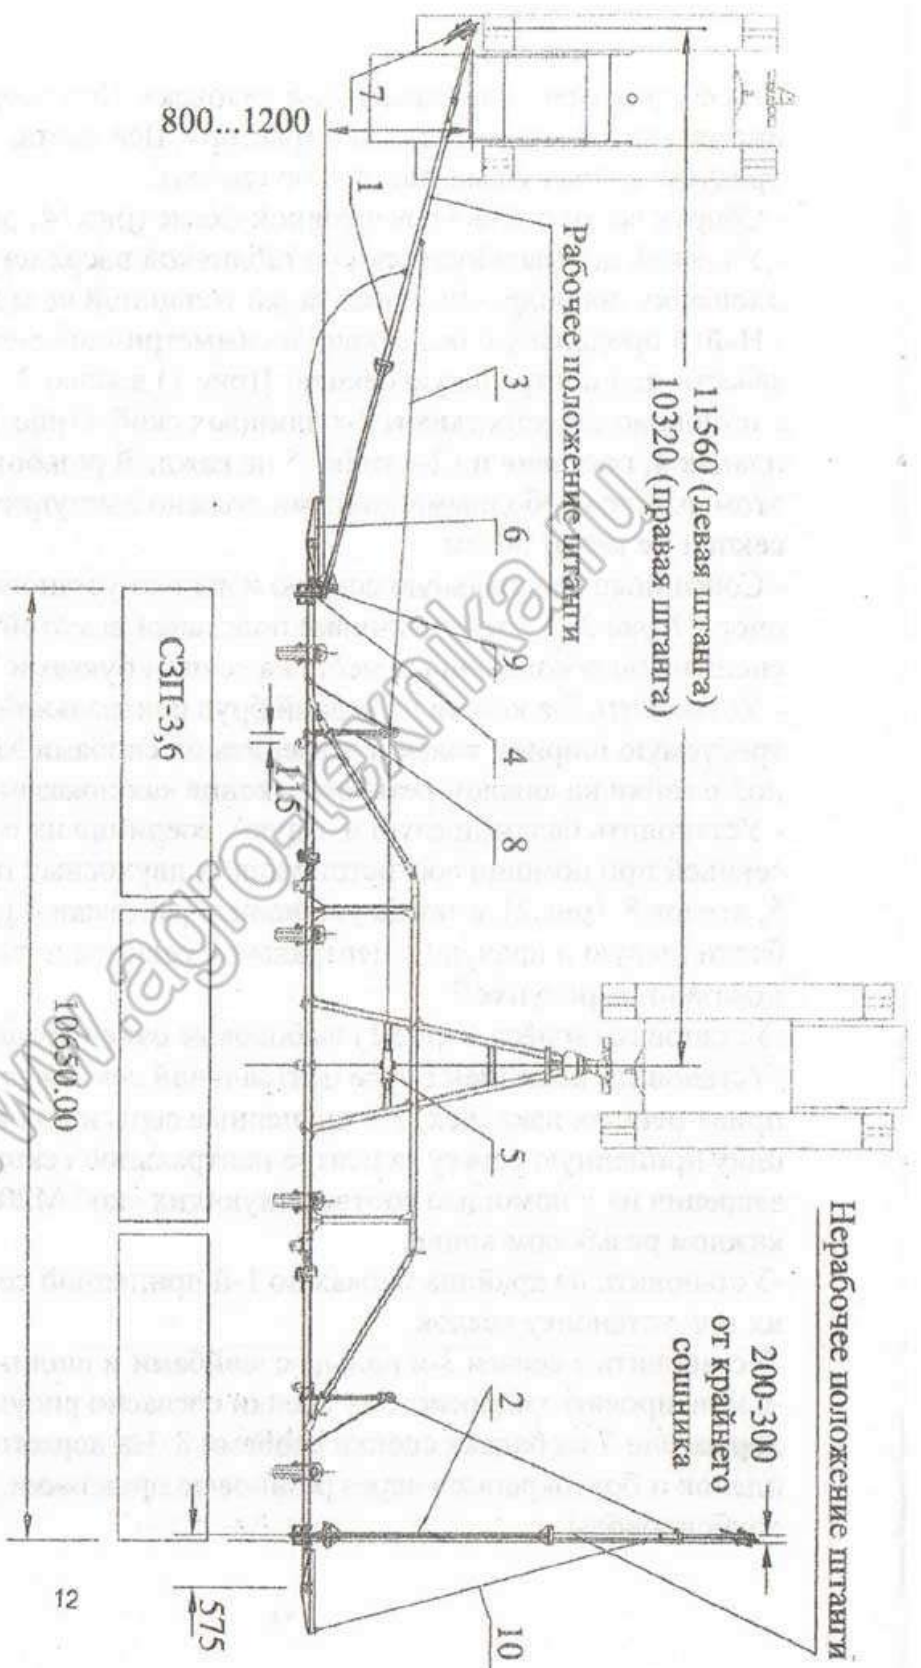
Схема установки маркера для 3-х осевого агрегата.
